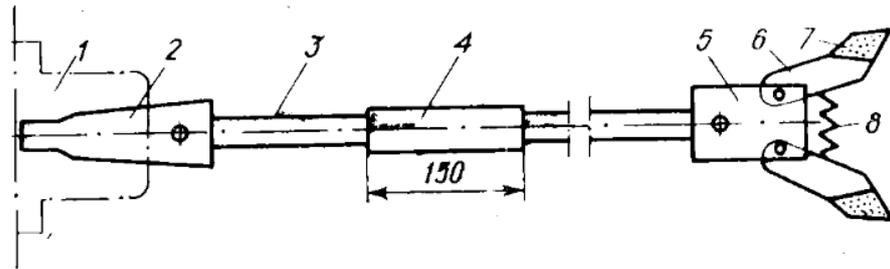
Приспособление для чистки труб: 1 – пневмодрель; 2 – конус Морзе; 3 – трубка; 4 – трубка-держатель; 5 – держатель резцов; 6 – резец; 7 – победитовый наконечник; 8 – пружина.
